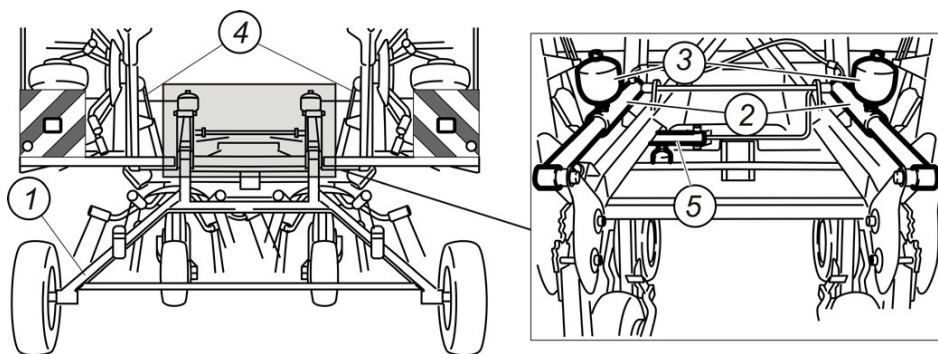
Схема расположения гидроцилиндров колесного хода:
